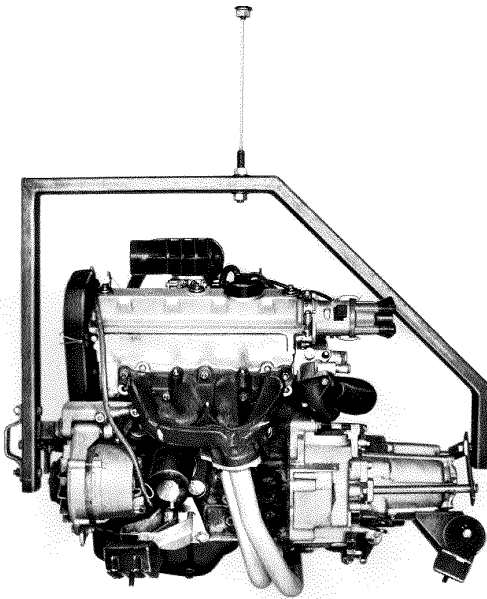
Aufhängung eines Kraftfahrzeugmotors
